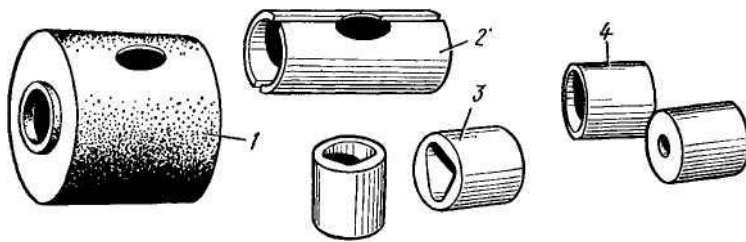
Термитный патрон марки ПА для сварки жил кабелей и изолированных проводов:
